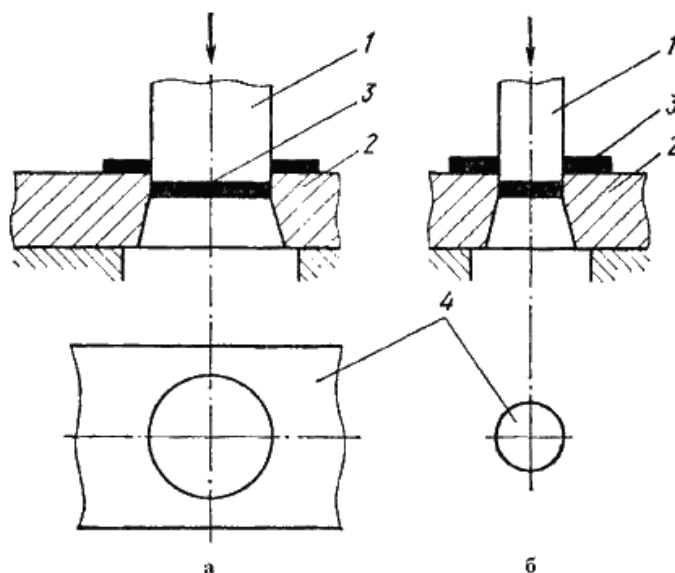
Схема процессов выруб-ки (а) и пробивки (б)
